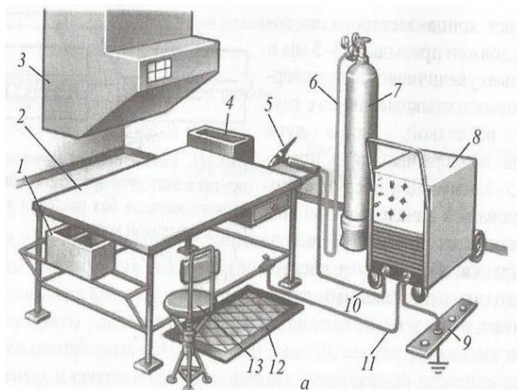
Общий вид сварочного поста для TIG-сварки
